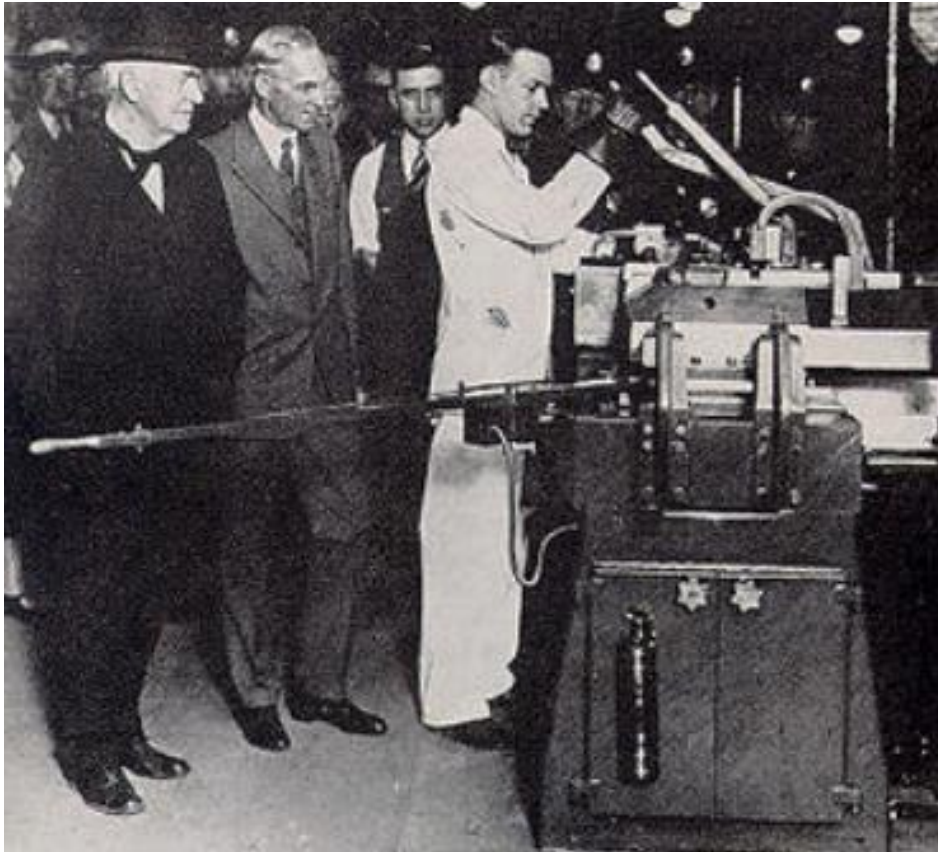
Henry Ford (seguido desde la derecha) muestra a Thomas Edison (izquierda) un operador utilizando una soldadora a tope en su planta.
